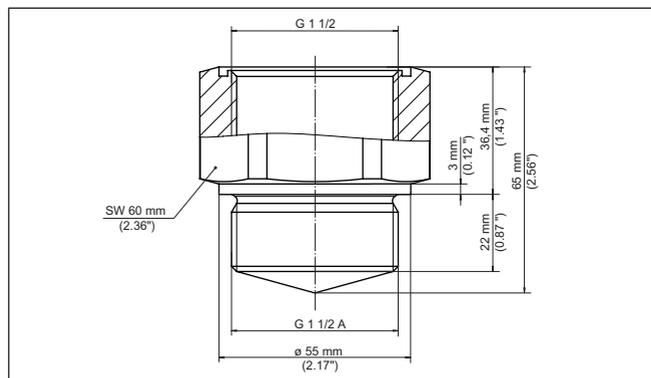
Medidas adaptador de rosca G1½ (DIN 3852-X) em rosca G1½, G2 (DIN 3852-X)
